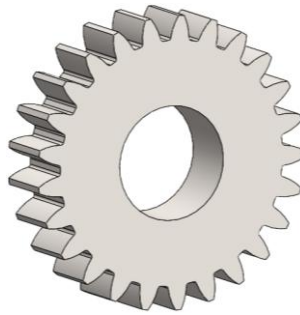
Modelo geométrico CAD 3D del engrane planeta.
